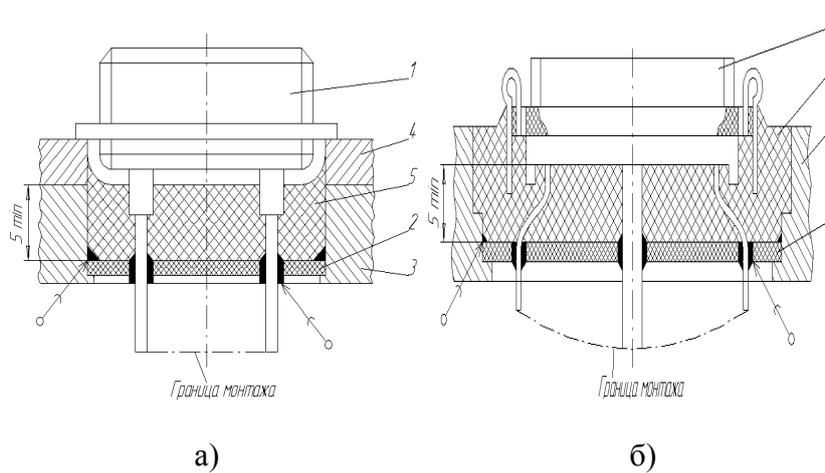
Герметизация вилки разъёма РСГ (а) и РПС1 (б) опайкой платы и заливкой компаундом: 1 – вилка разъёма; 2 – монтажная плата; 3 – корпус блока; 4 – прокладка; 5 – компаунд
